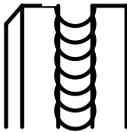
Efecto del rodillo en el alambre de soldadura
